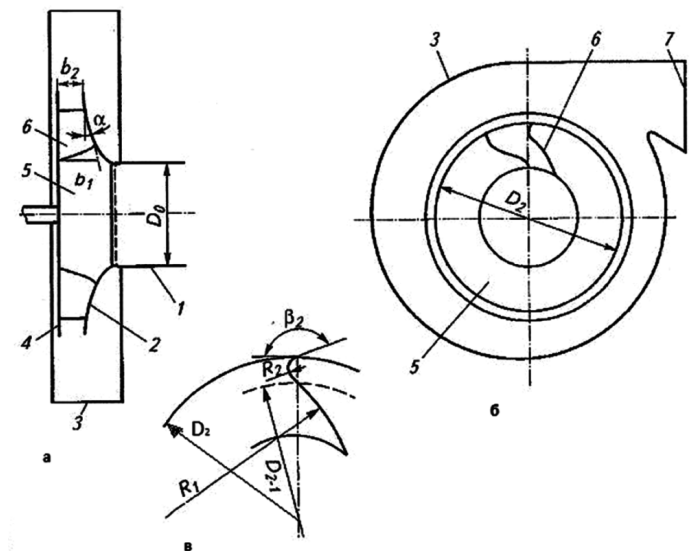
Воздушный центробежный вентилятор с оптимальными значениями основных геометрических параметров проточной части: 1 - входной патрубок, 2 - передний диск, 3 – корпус вентилятора, 4 – задний диск, 5 – рабочее колесо, 6 – лопатки рабочего колеса, 7 – выходной патрубок.
